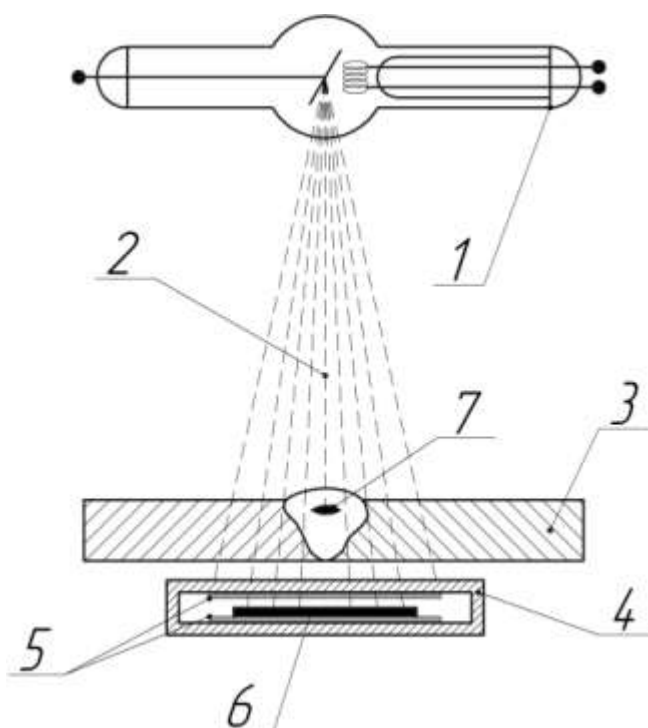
Схема просвечивания рентгеновскими лучами: 1 – рентгеновская трубка; 2 – рентгеновское излучение; 3 – сварное соединение; 4 – кассета; 5 – усиливающие экраны; 6 – фотопленка; 7 - дефект.
